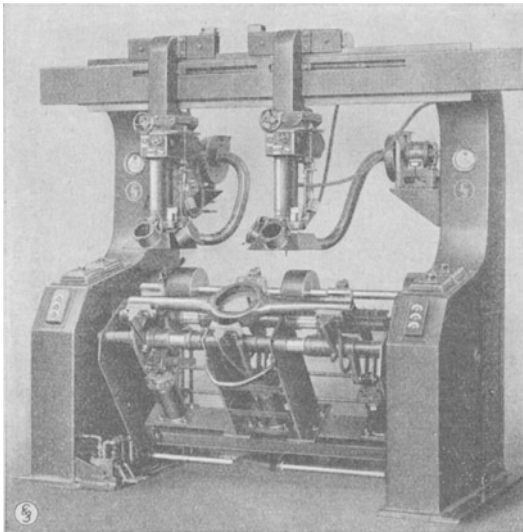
Selbsttätige Schweißmaschine für Hinterachsbrücken.
